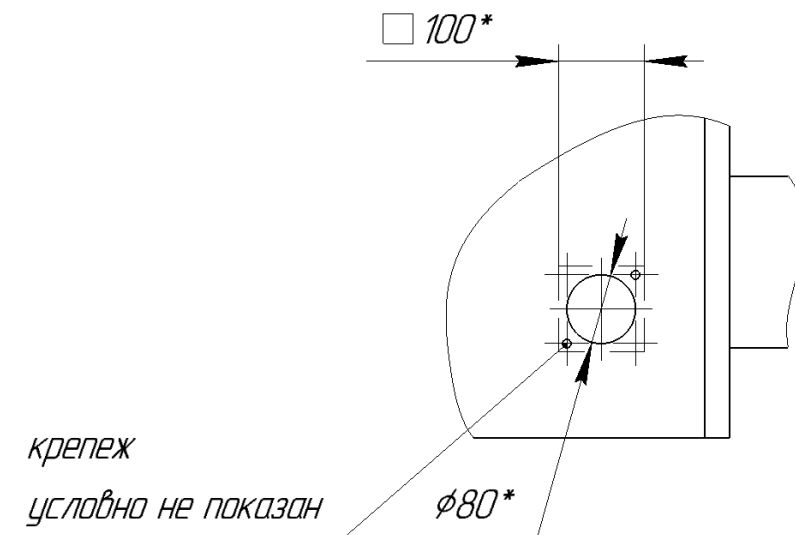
Вид снизу выключателя. Размеры пластины.
